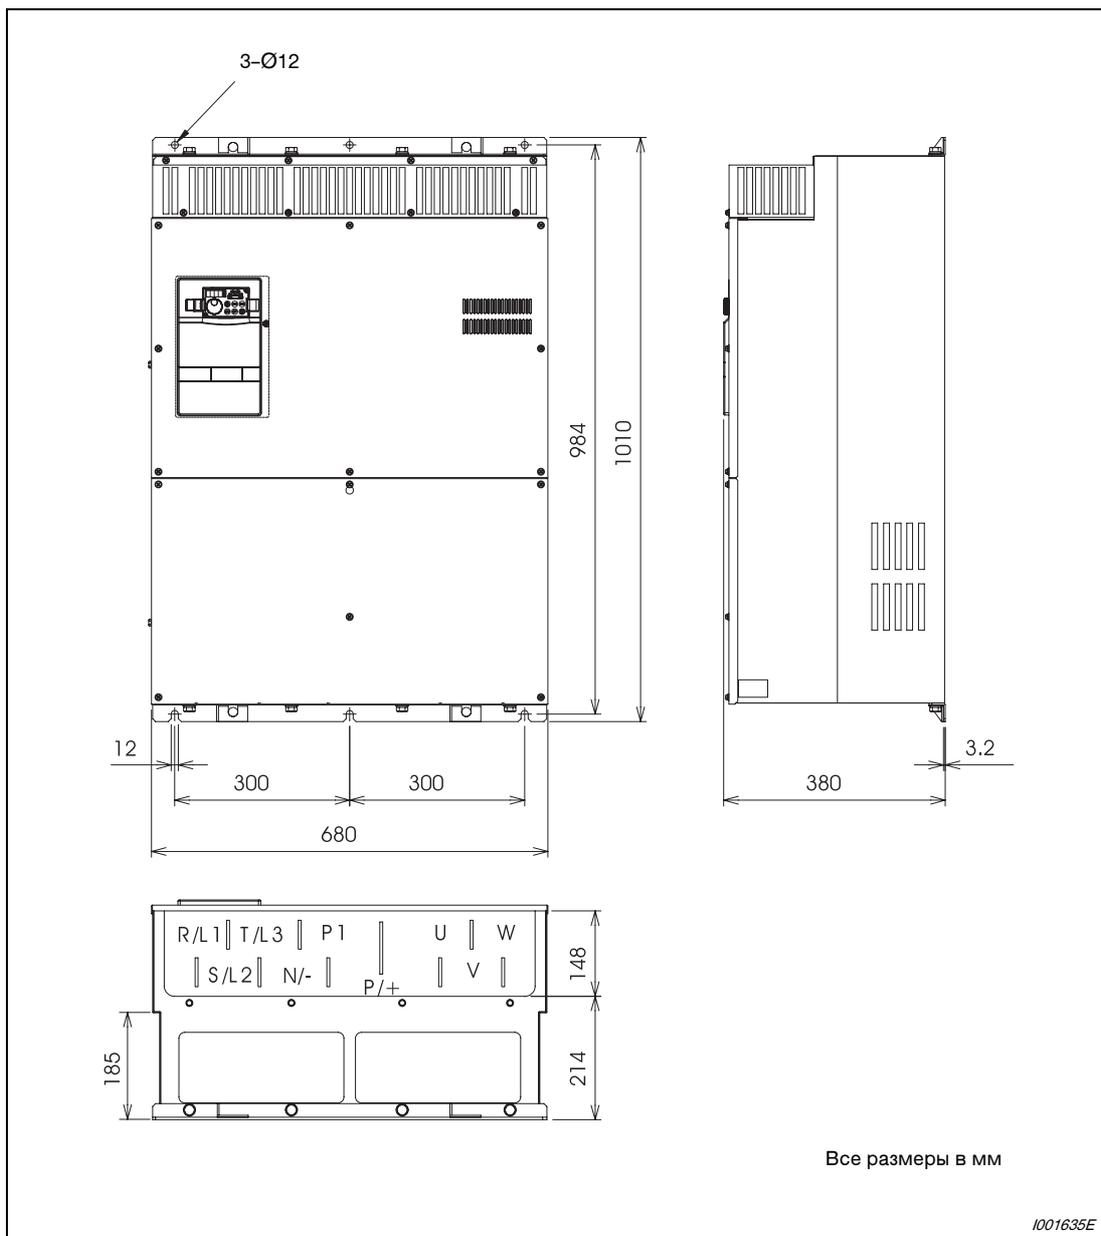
Размеры FR-A 740-05470, FR-A 740-006100 и FR-A 740-06830
